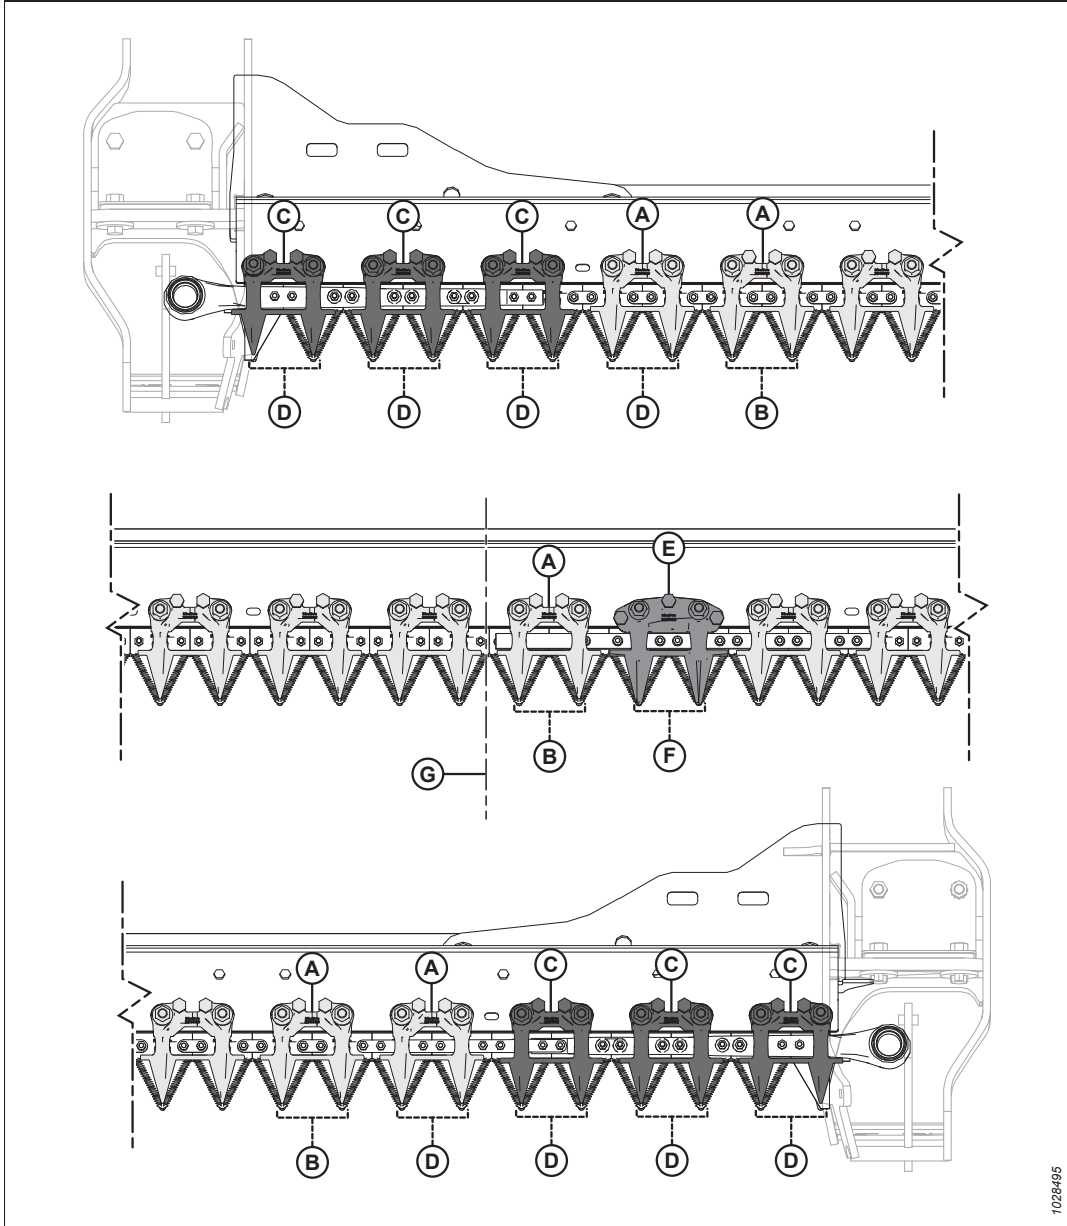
Местоположение укороченных противорежущих пальцев и прижимов — жатки с двойными ножами
